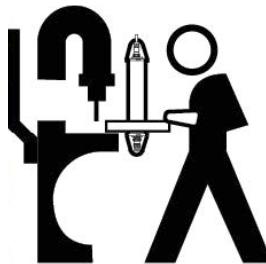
Restricción de acceso a la máquina por la parte frontal
